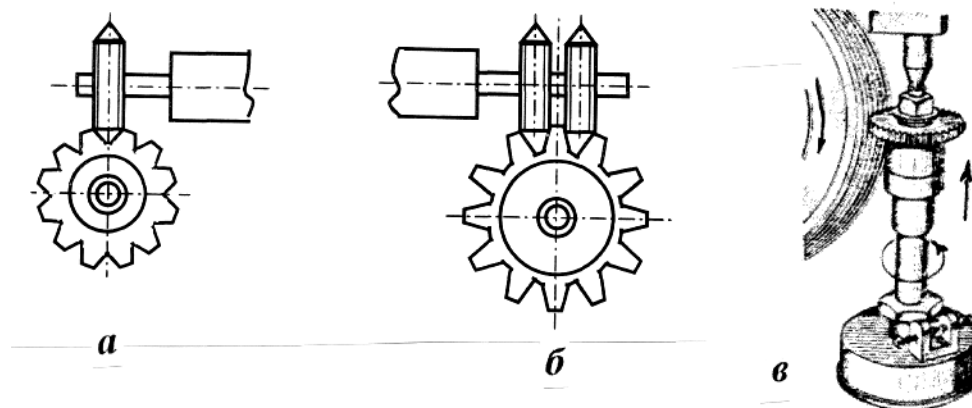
Зубошлифование цилиндрических зубчатых колес: а - на станке 5851 одним конусным кругом; б - двумя абразивными кругами; в - на станке МАТРИКС червячным абразивным кругом.
